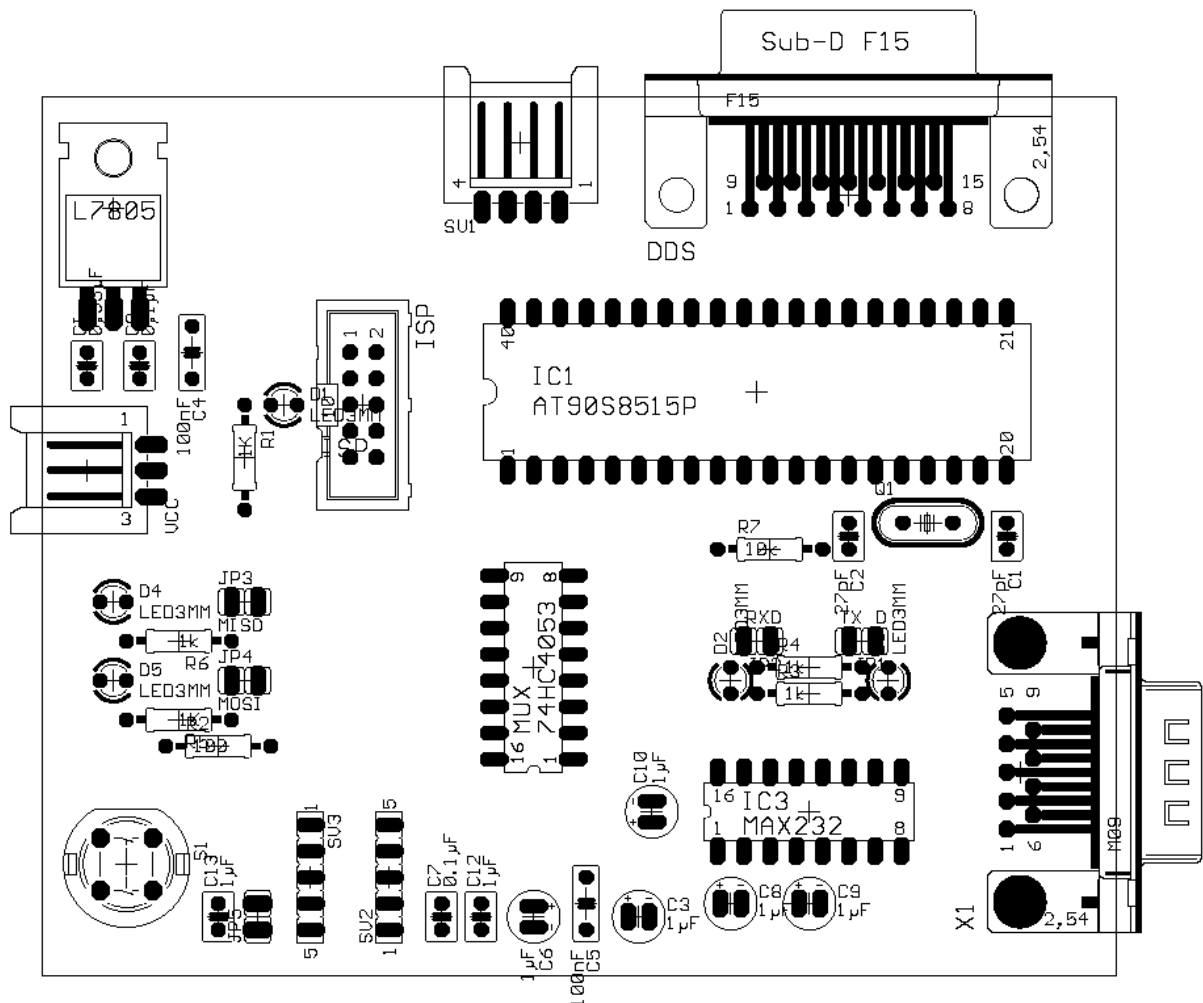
Bestückungsansicht des Platinen-Layouts
